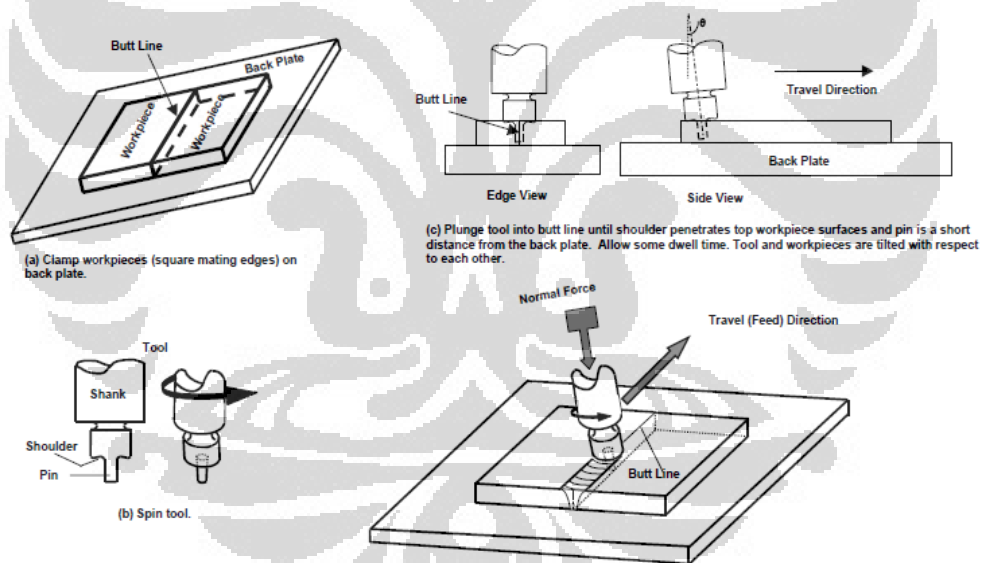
Gaya-gaya pada friction stir welding
